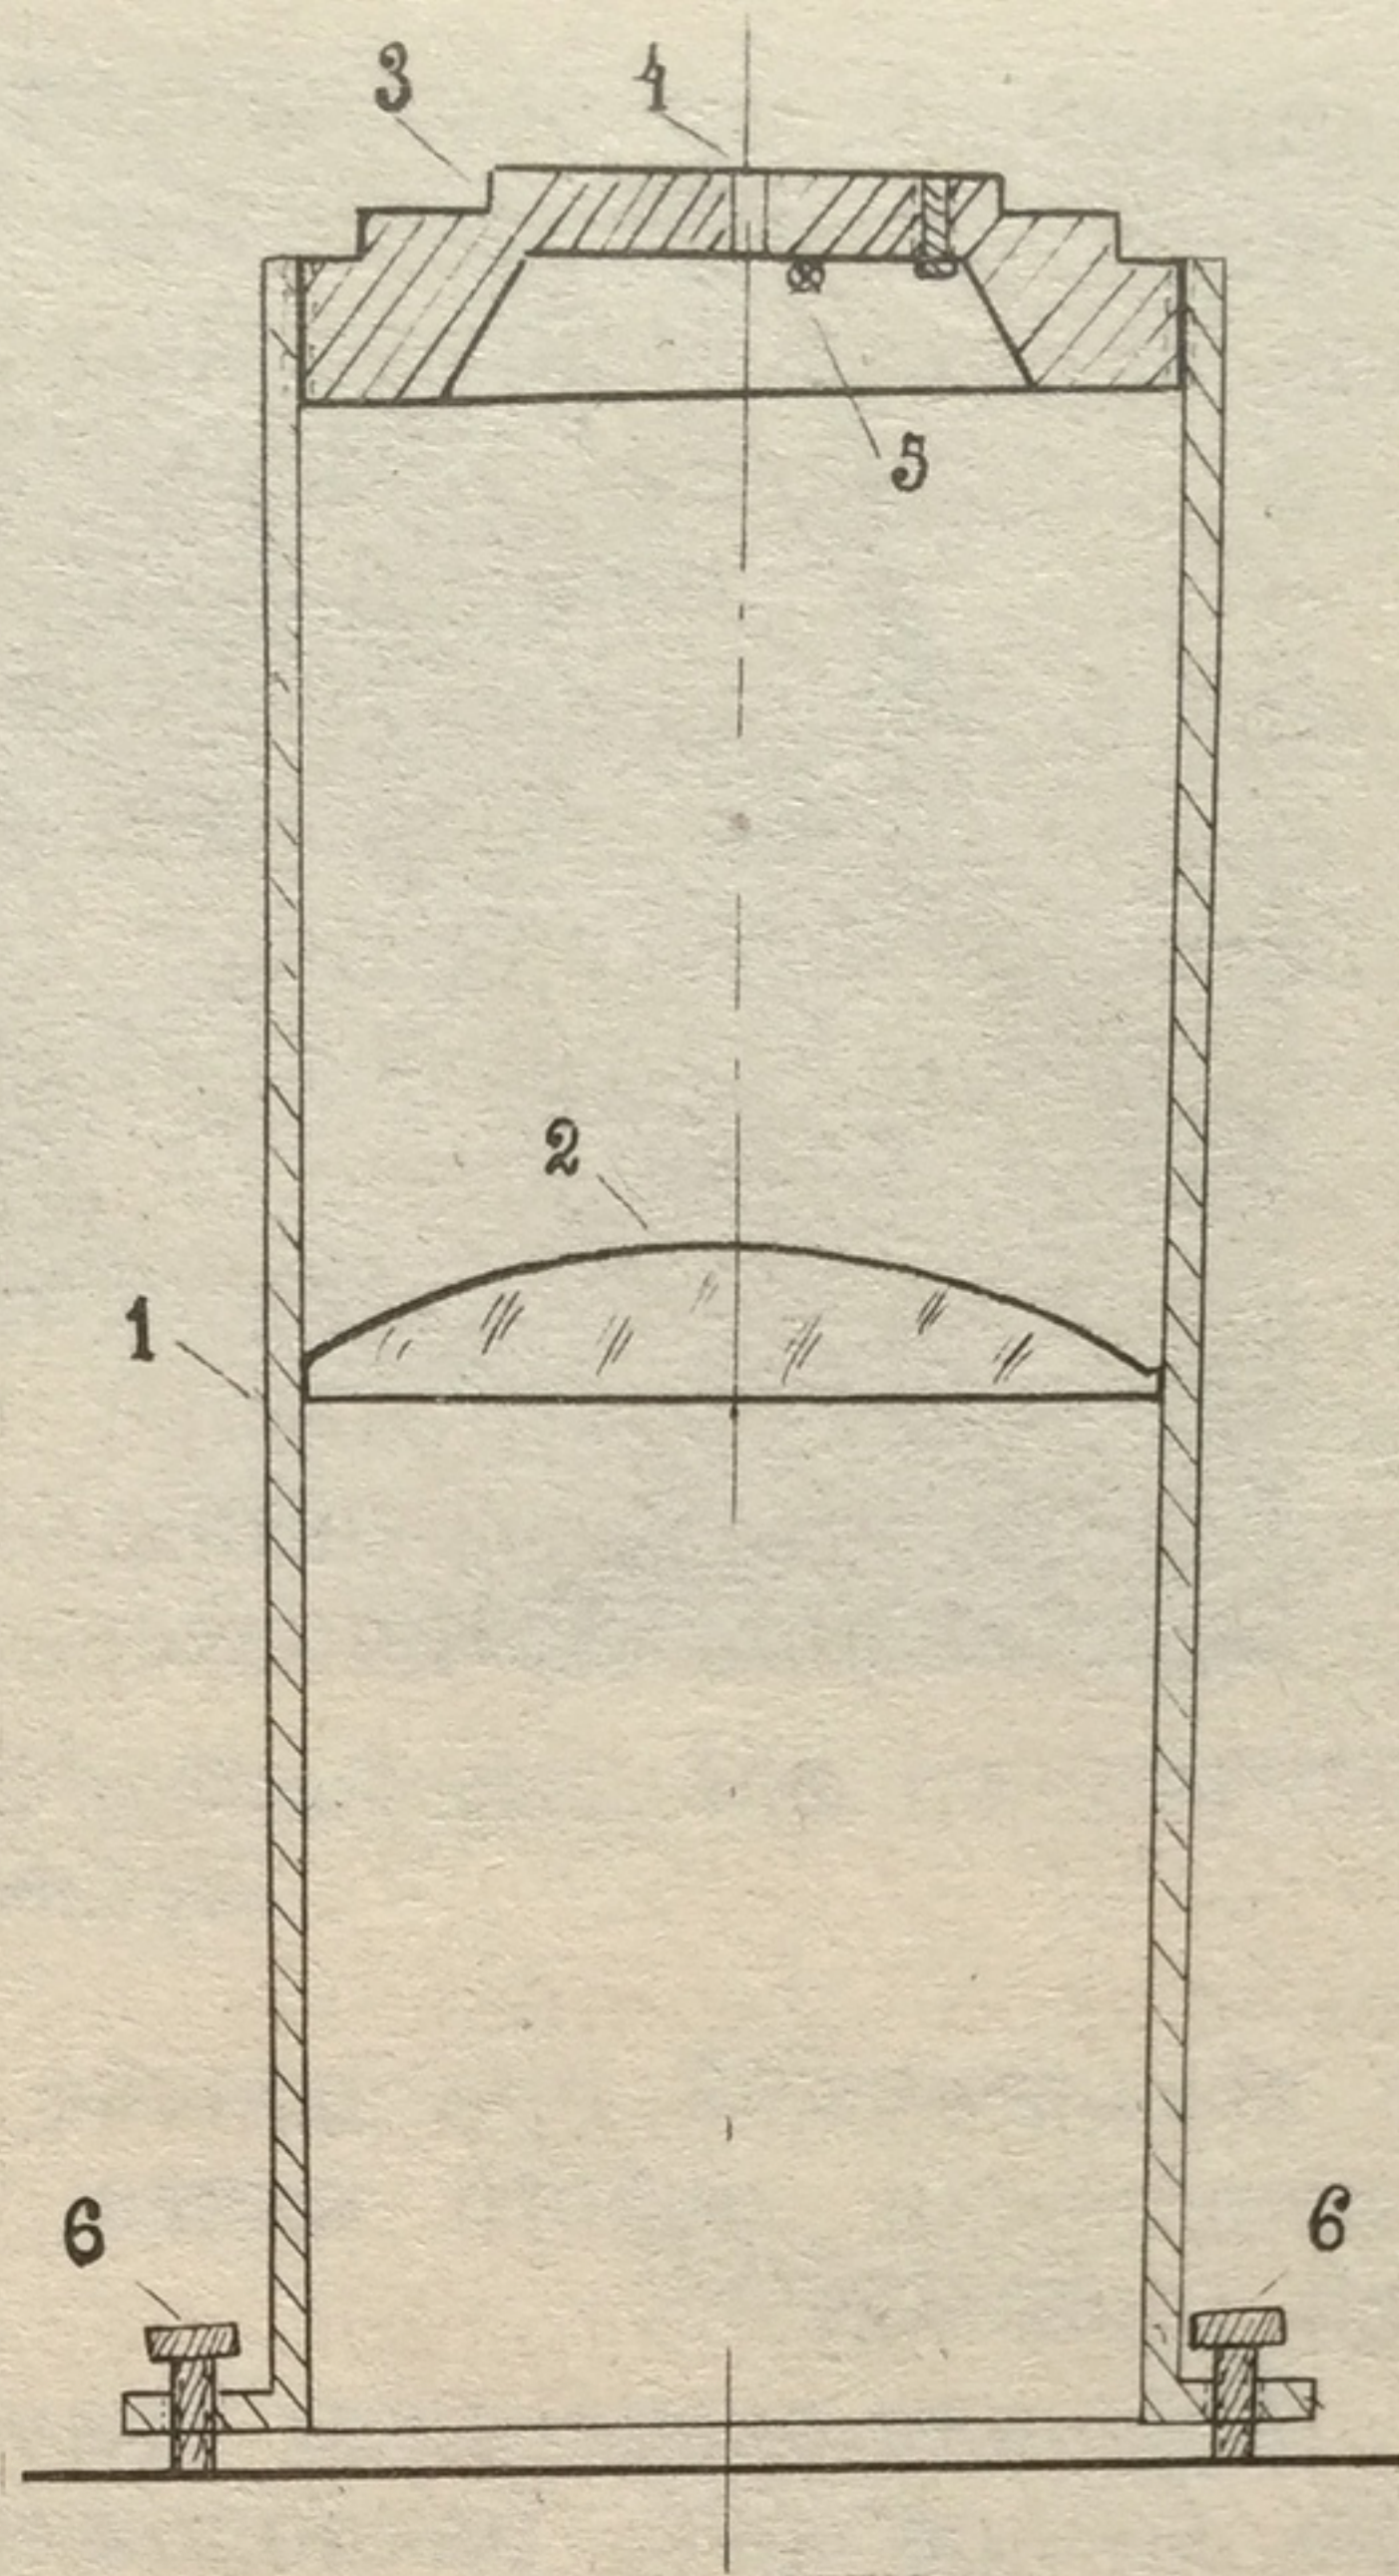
Чертеж конструкции приставки 3: 1. Корпус приставки; 2. Линза; 3. Диафрагма; 4. Отверстие диафрагмы; 5. Источник освещения; 6. Регулировочные винты
